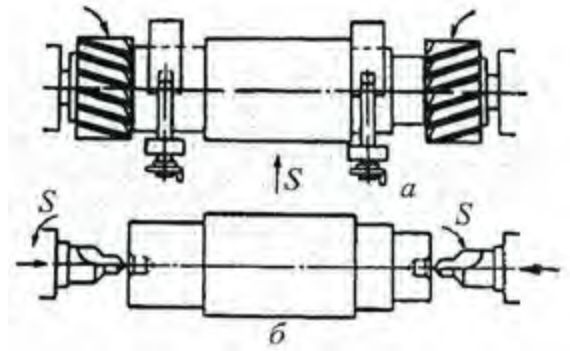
Схеми оброблення торців валів на фрезерно-центральних верстатах
